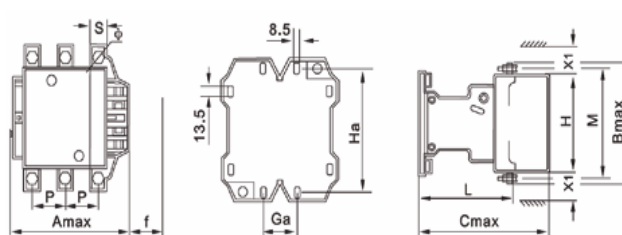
Габаритные и установочные размеры контакторов серии КМ-102 400-500А, мм.
